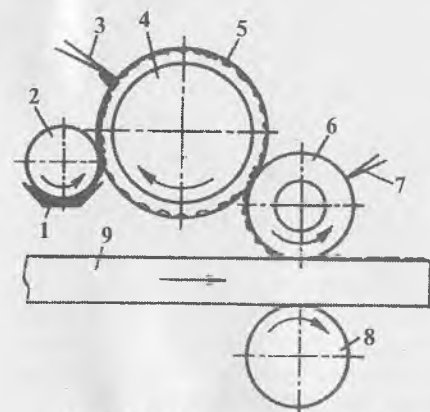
Схема станка для глубокой печати текстуры древесины на поверхности заготовки:
